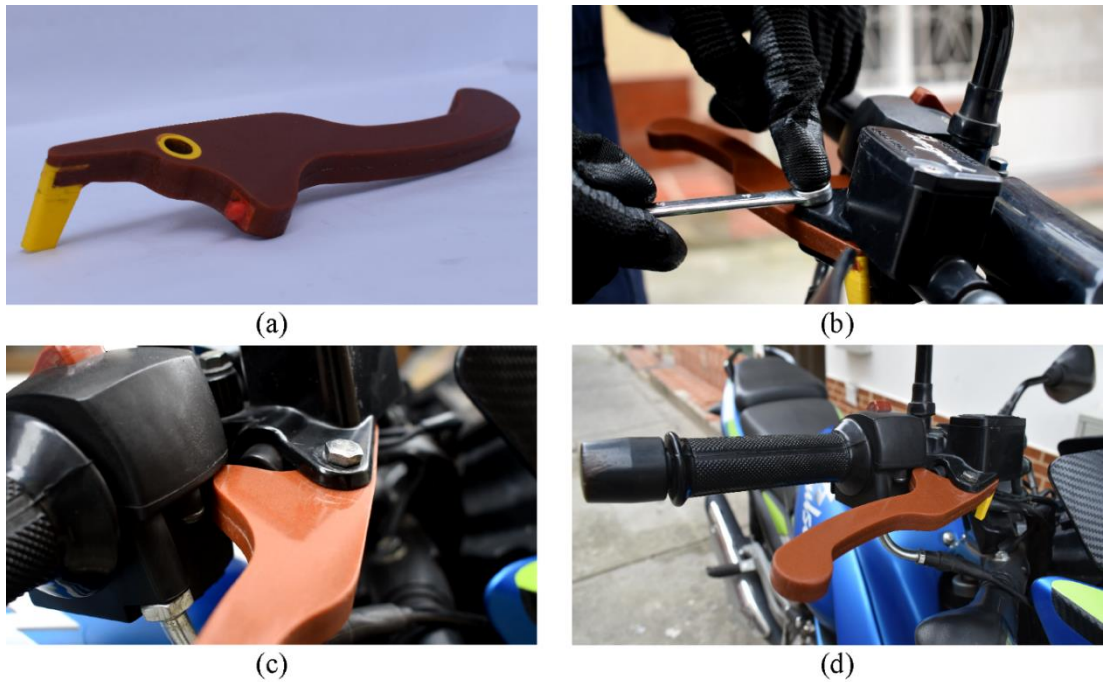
Montaje de la leva de freno: (a) Pieza desmoldada. (b) Ajuste de la pieza. (c) Acercamiento a la bomba de inyección del líquido de frenos. (d) Ensamblaje completo de la leva de freno.
